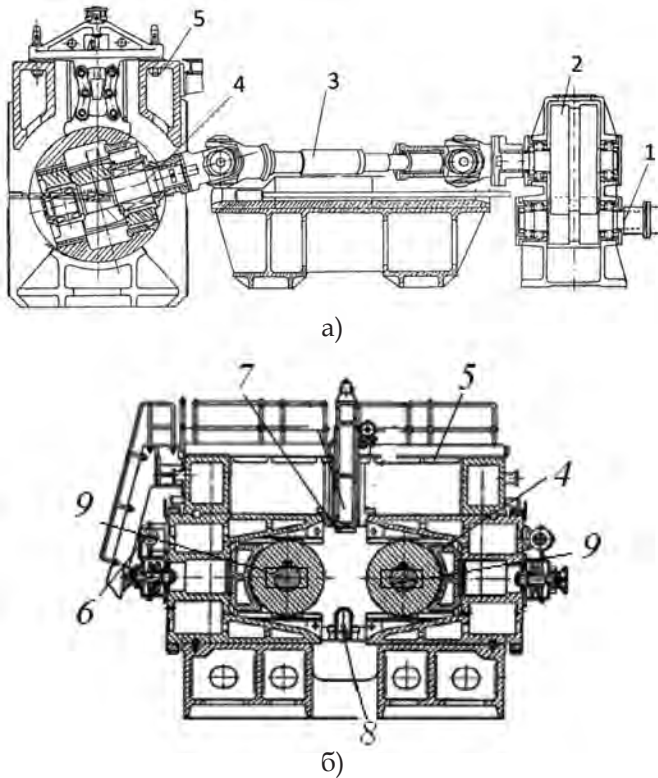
Главный привод (а) и рабочая клетка (б) прошивного стана ТПА
